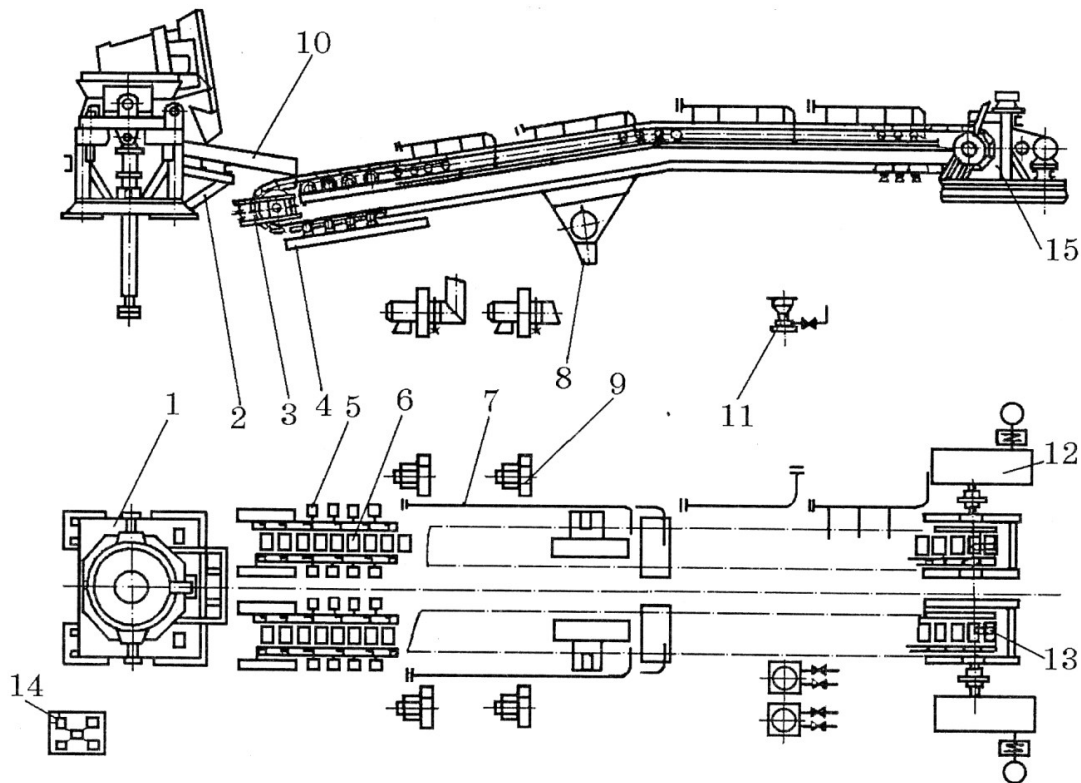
Схема розливочної машини МРФ-4-722-270: 1 – кантувальний пристрій; 2 – похилі плити ; 3 – натяжна станція; 4 – рама; 5 – роликовий пристрій; 6 - стрічка конвеєра з виливницями; 7 – водяне охолодження виливниць; 8 – оприскувач; 9 – пристрій димососу; 10 – розливний жолоб; 11 – система змастилення; 12 – система приводу конвеєра; 13 – жолоб скидання; 14 – пристрій гідравлічного приводу
